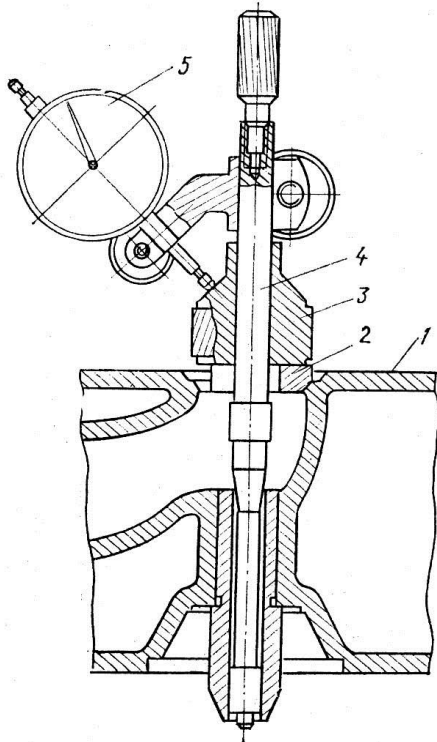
Схема перевірки биття робочої фаски клапанного гнізда відносно поверхні отвору напрямної втулки клапана:
